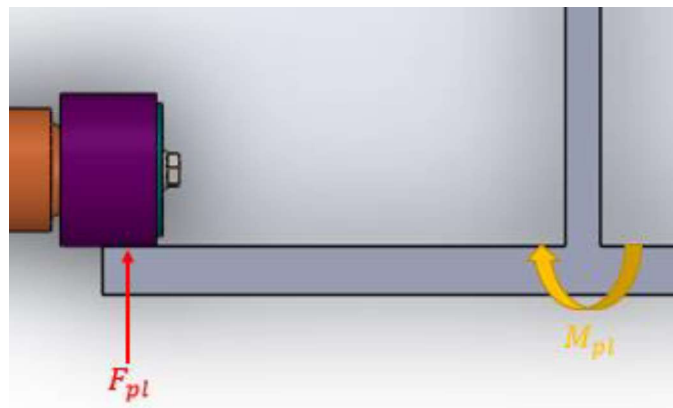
Momento plástico por efecto de la soldadura.
